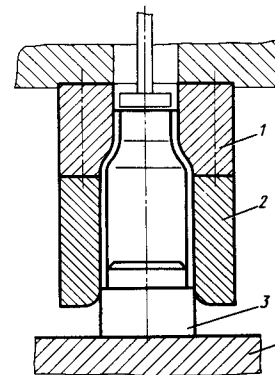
Конструктивная схема штампа для обжима детали, показанной на рис. 18: 1 — матрица; 2 — обойма; 3 — опора; 4 — выталкиватель
